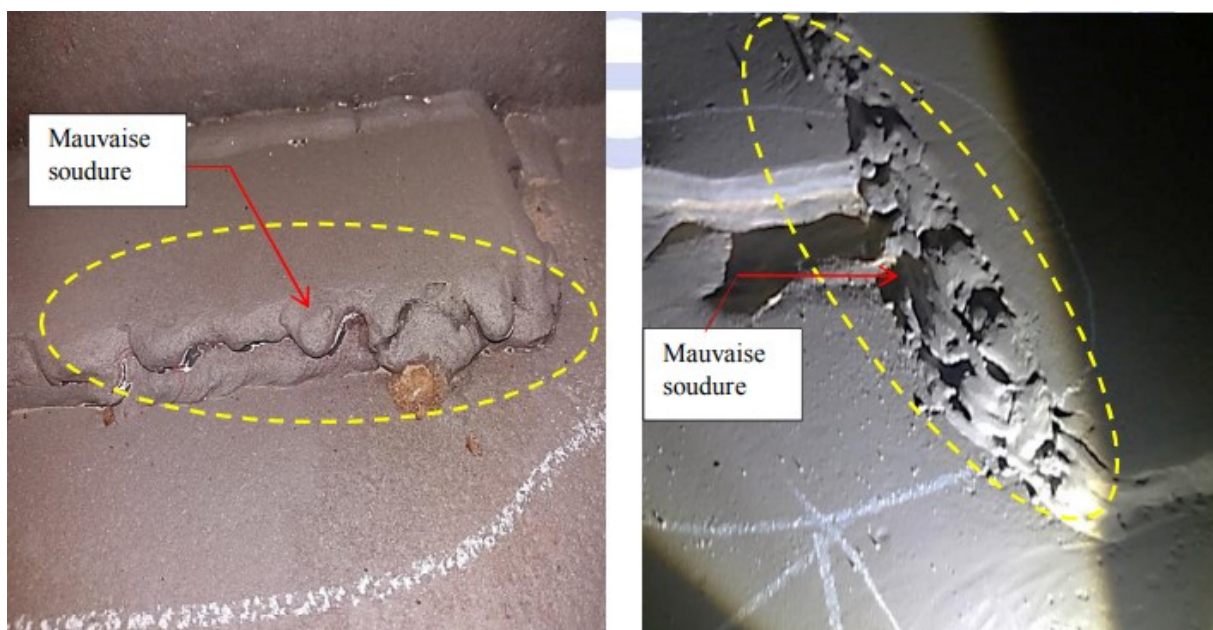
Mauvaise soudure qui peut présenter des points faibles pour la corrosion
